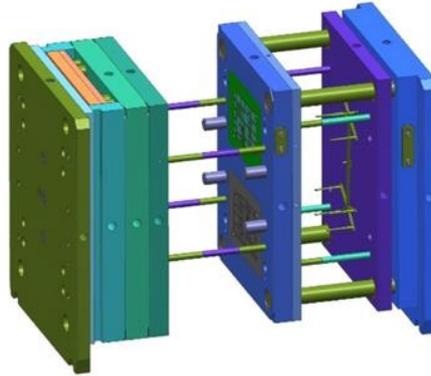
molde de tres placas. Fuente: hsmolds [29]
